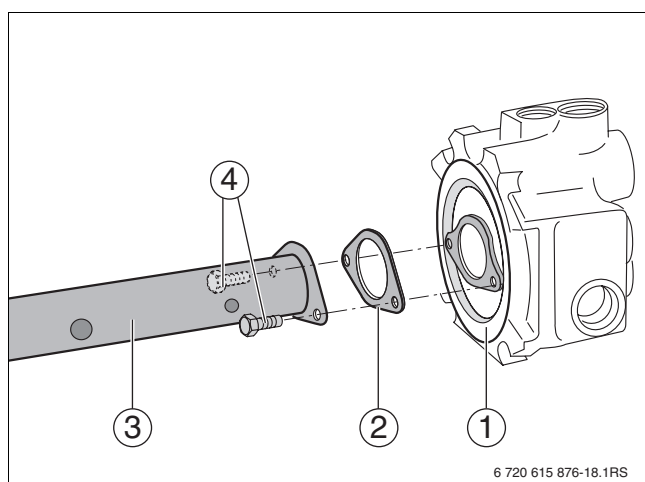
Monter le tube injecteur sur la pièce de raccordement spécifique
